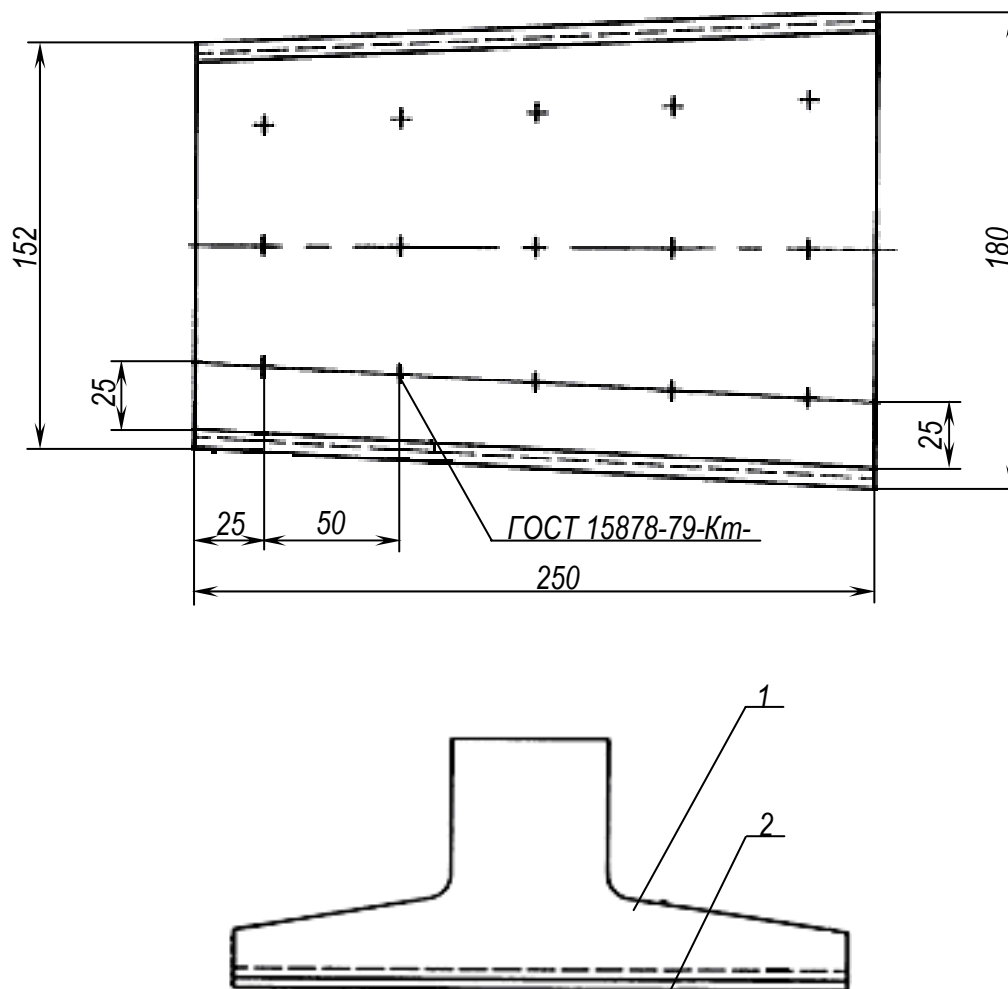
Скоба: 1 – скоба; 2 – планка
